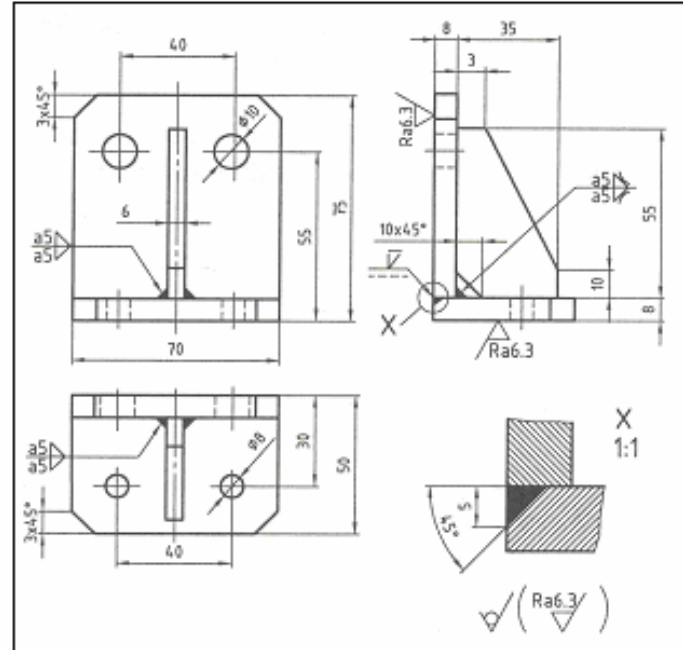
Kaynak dikişlerinin çizimle gösterilmesi
